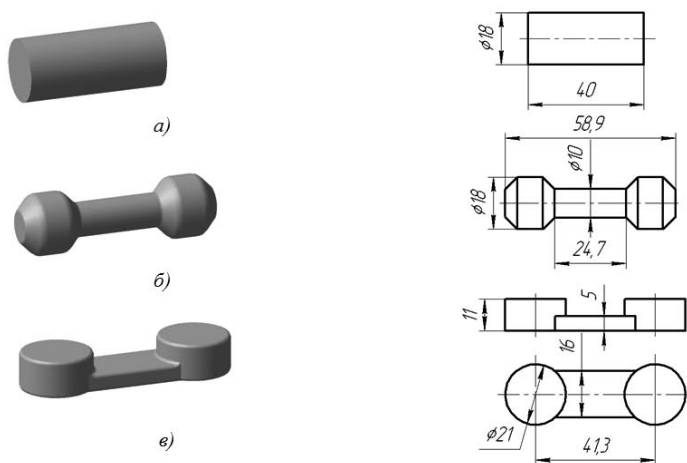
Переходы изготовления звена цепи ОК 5056Б комплексной технологией прокатки-штамповки
